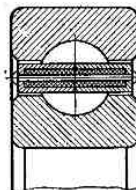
Шарикоподшипник, с сепаратором которого запрессована твердая смазка
